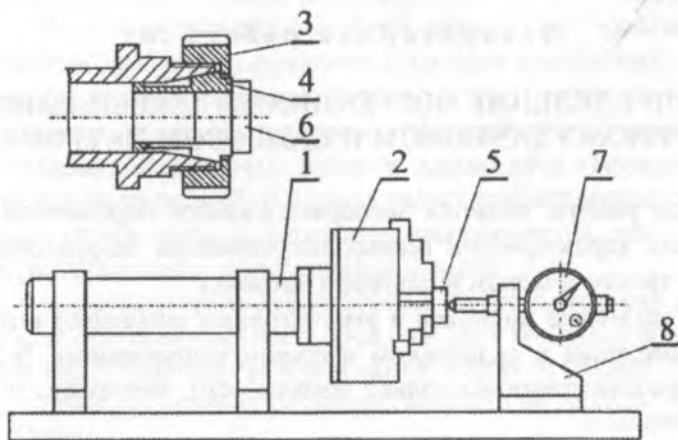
Схема приспособления для определения погрешности закрепления заготовки
